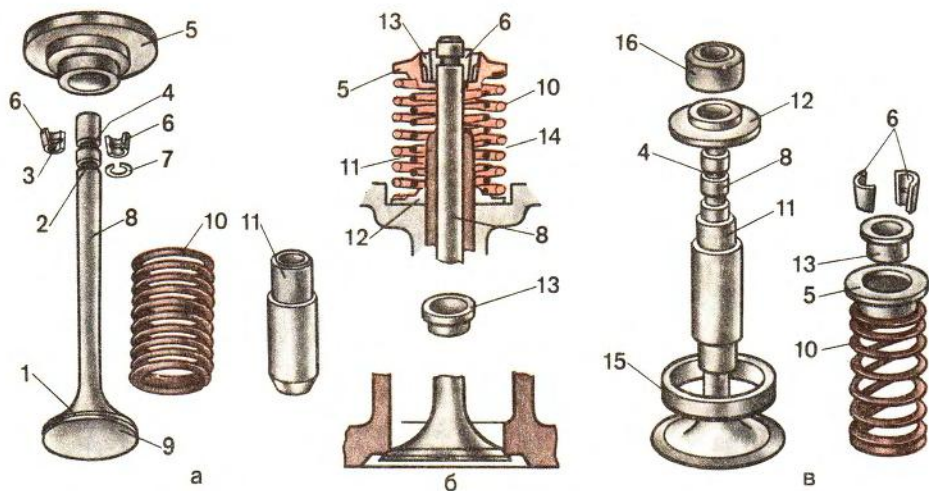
Клапан, пружина и детали ее крепления в механизме газораспределения:
